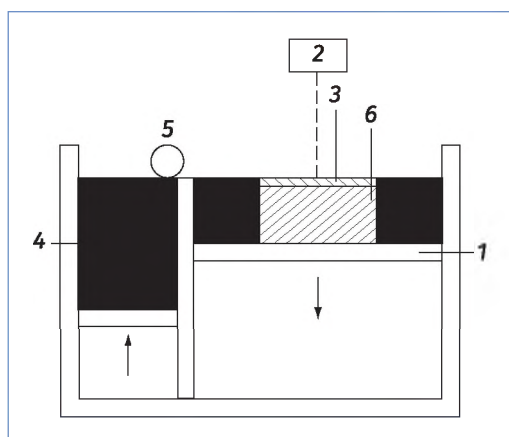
Схематическое представление InkJet-технологии: 1 – платформа построения; 2 – печатающая головка; 3 – новый слой детали; 4 – платформа с материалом; 5 – вал; 6 – деталь
